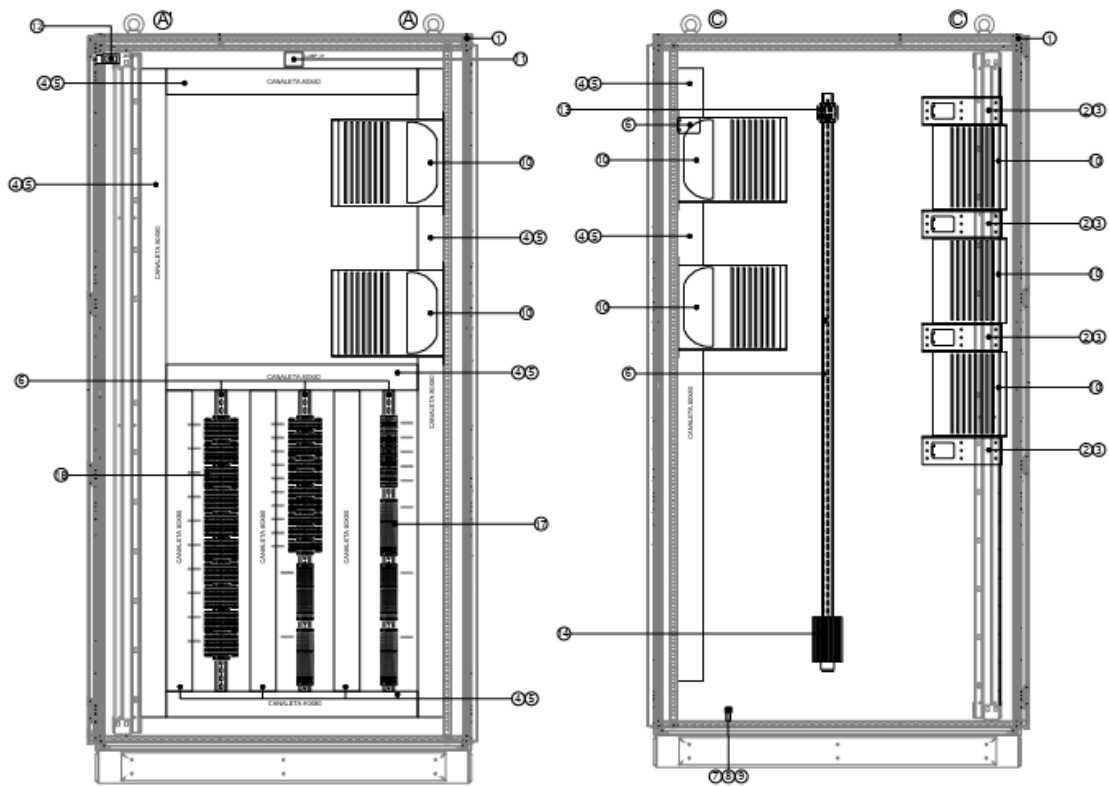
Vistas laterales Gabinete Deslaste Esclavo SS01.
